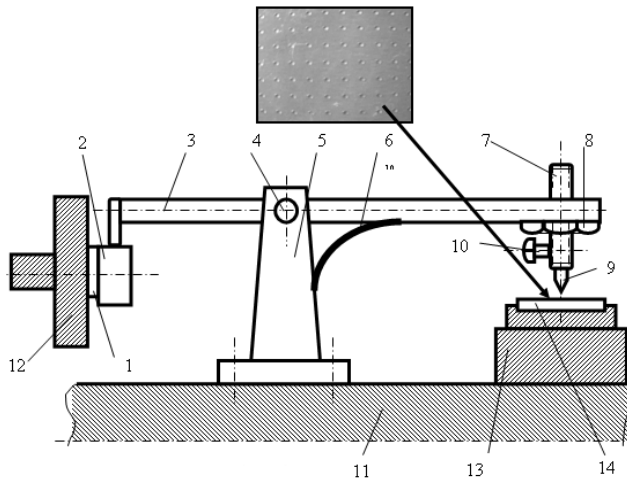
Пристрій для утворення лунок: 1 – приводний вал; 2 – кулачок; 3 – коромисло; 4 – вісь коромисла; 5 – стояк осі коромисла; 6 – пружина; 7 – регулювальний гвинт; 8 – контргайка регулювального гвинта; 9 – бойок; 10 – механізм кріплення бойка; 11 – основа; 12 – патрон; 13 – механізм переміщення; 14 – деталь (зразок)
